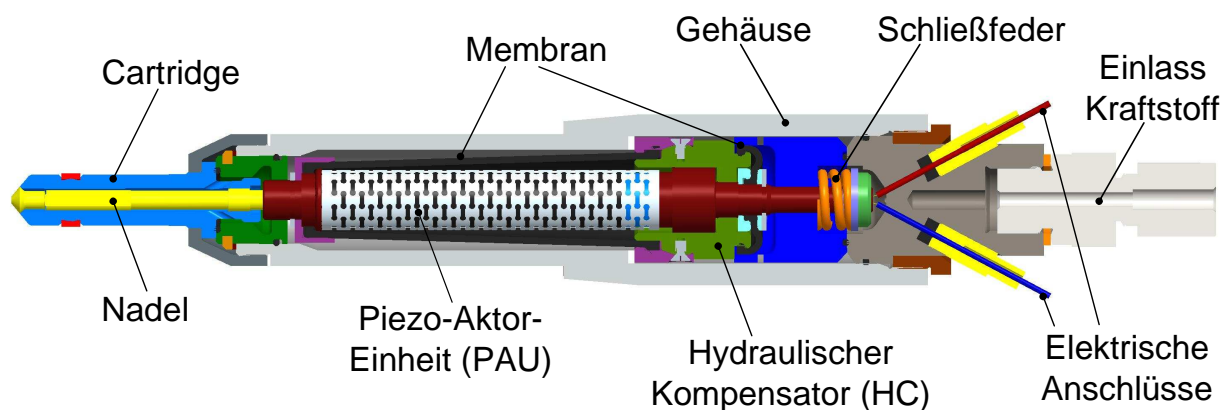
Übersicht des aufgebauten Injektors für die Zylinderdruckmessung
